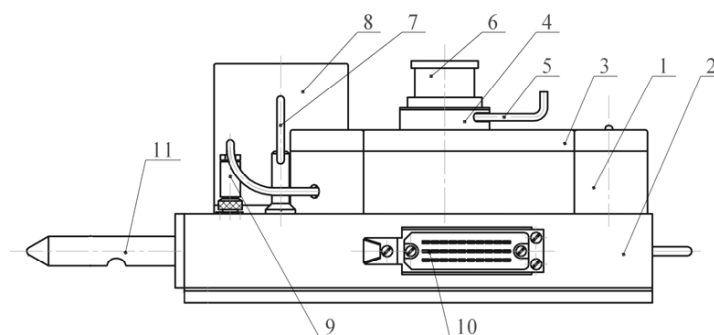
Измерительный модуль КПЭЛ, КТВЭЛ (вид сбоку): 1 – блок измерительный; 2 – привод; 3 – крышка блока измерительного; 4 – зажим эксцентриковый; 5 – рукоятка зажима; 6 – центрирующая втулка; 7 – винт транспортный; 8 – колпак защитный двигателя; 9 – разъем с кабелем; 10 – разъем колодочный; 11 – узел дистанционного подсоединения модуля к ТОМ
